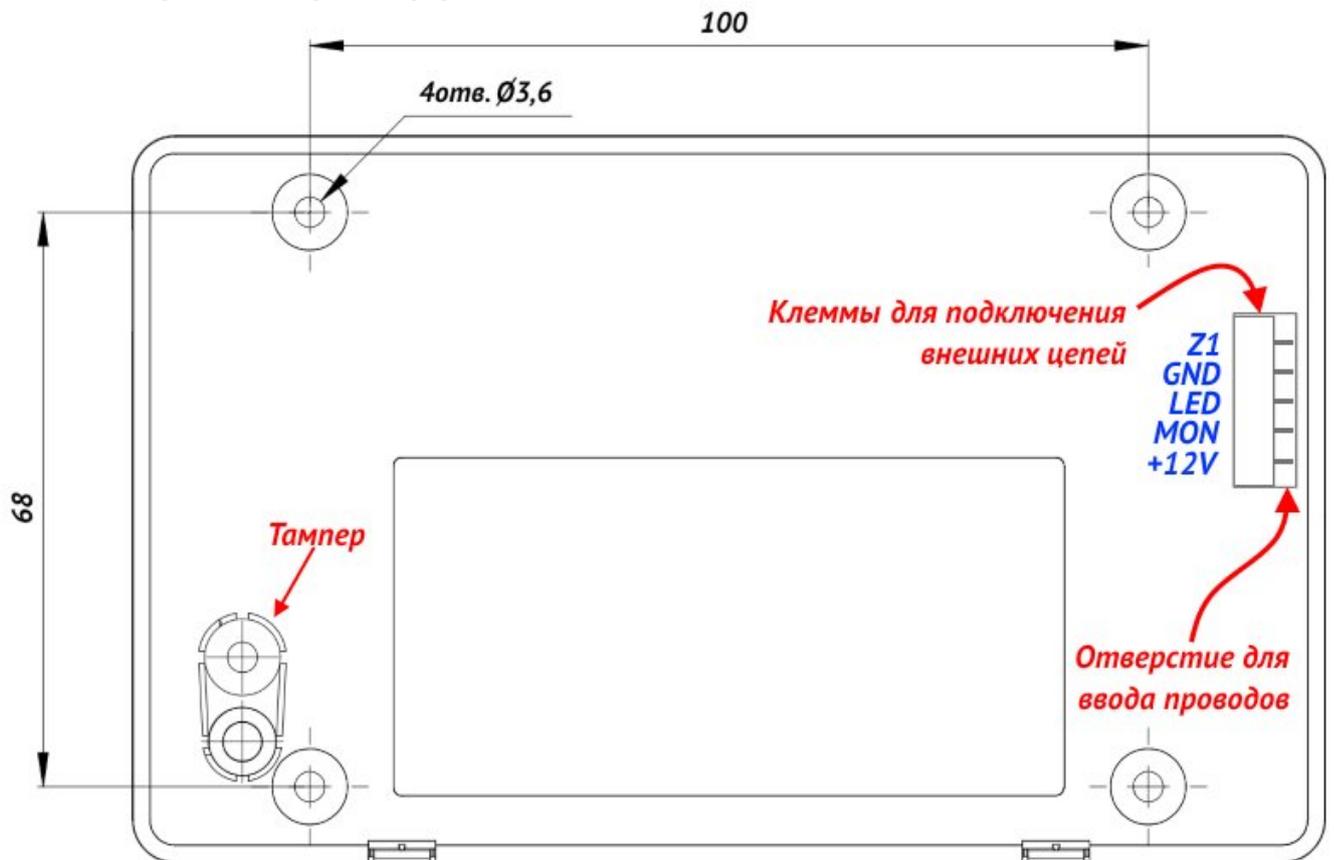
Внешний вид с обратной стороны корпуса и установочные размеры
